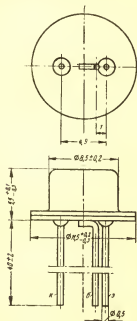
Габаритный чертеж транзисторов П16—П16Б.
